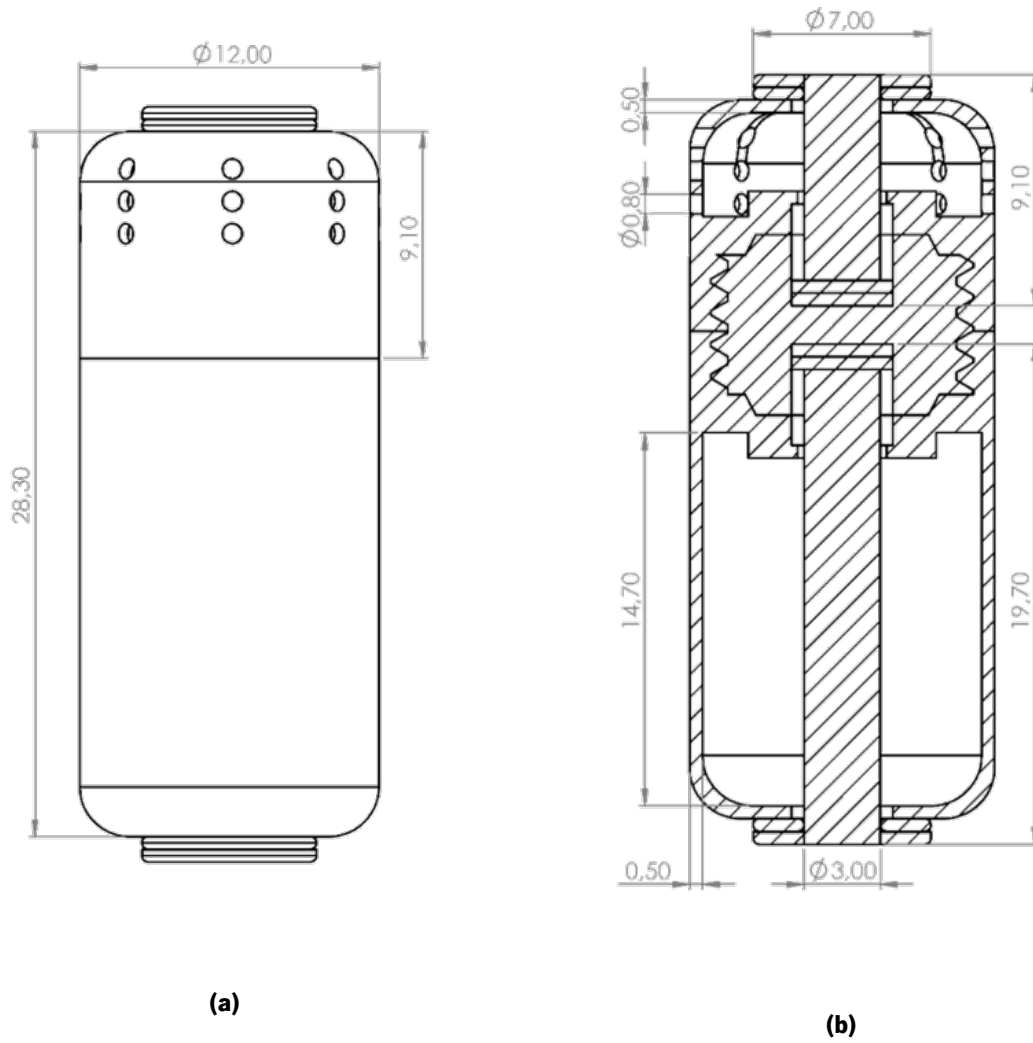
Design* CAD e dimensões (mm) do corpo da cápsula ingerível 1.0 (Disco 4 mm): a) vista lateral, b) vista em corte.
